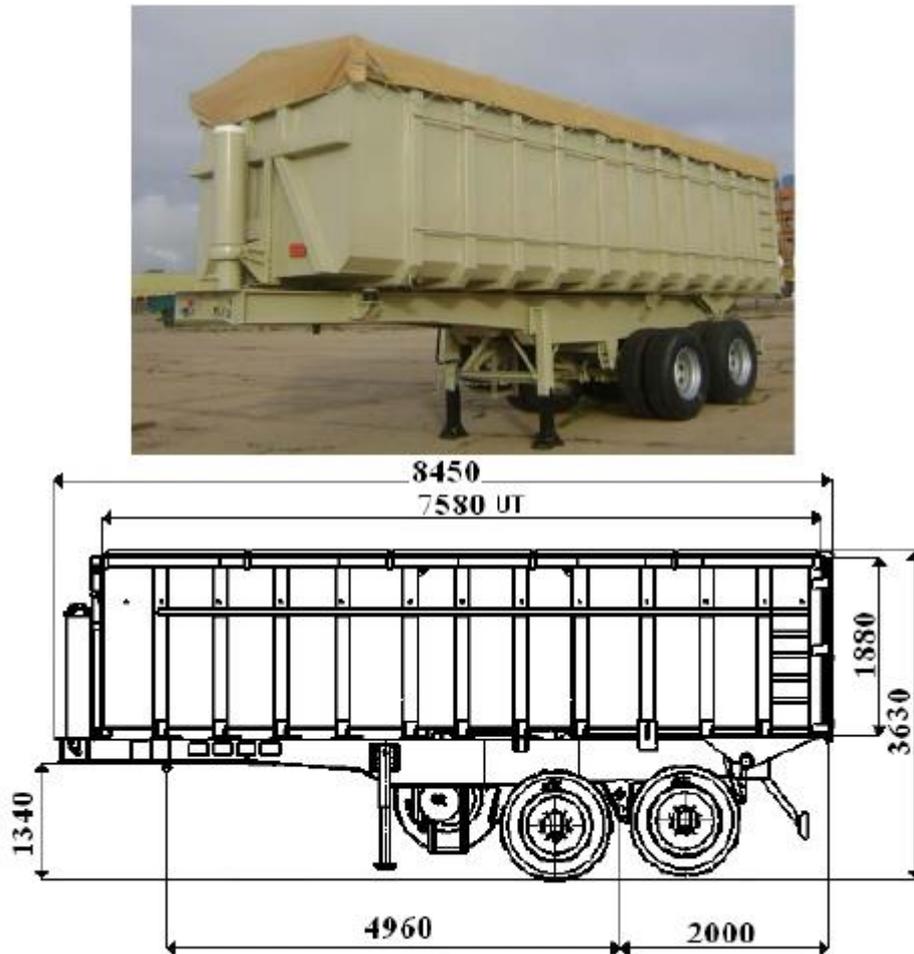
dessin de définition de la benne céréalière 31.5m³
